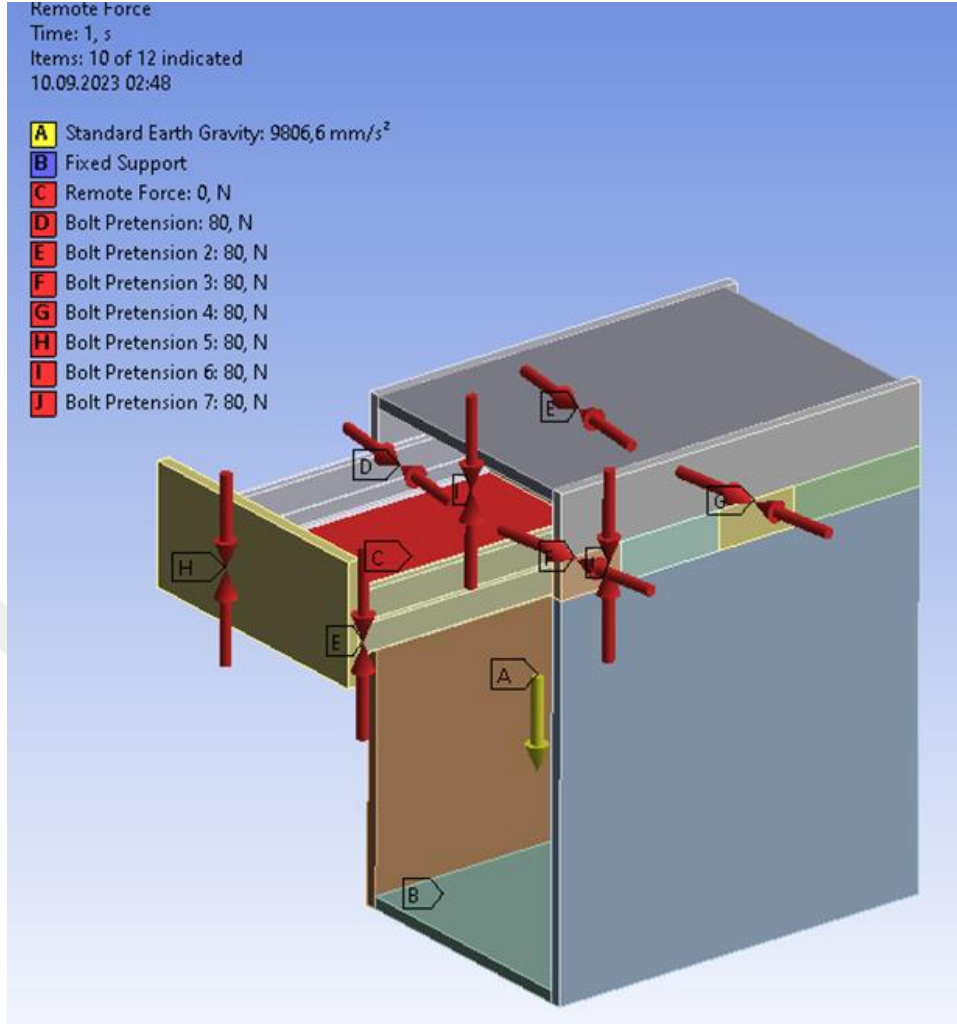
Çekmece Test 1 için sınır koşullarının belirlenmesi.
